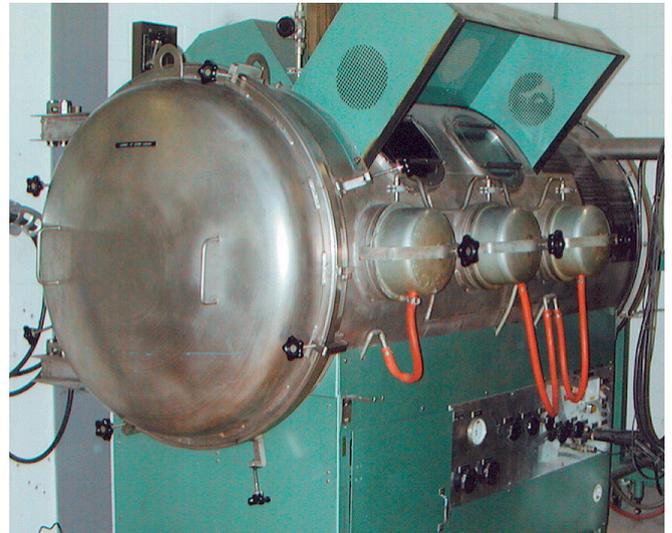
Schutzkammer zum Schweißen reaktiver Metalle (RUAG Emmen)
